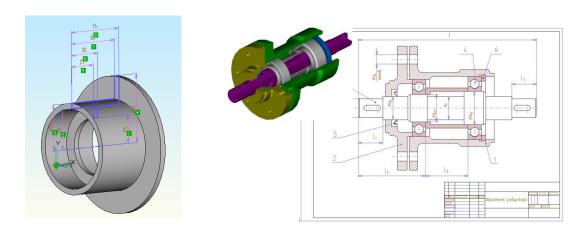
3 Омодель детали, сборка и сборочный чертеж
